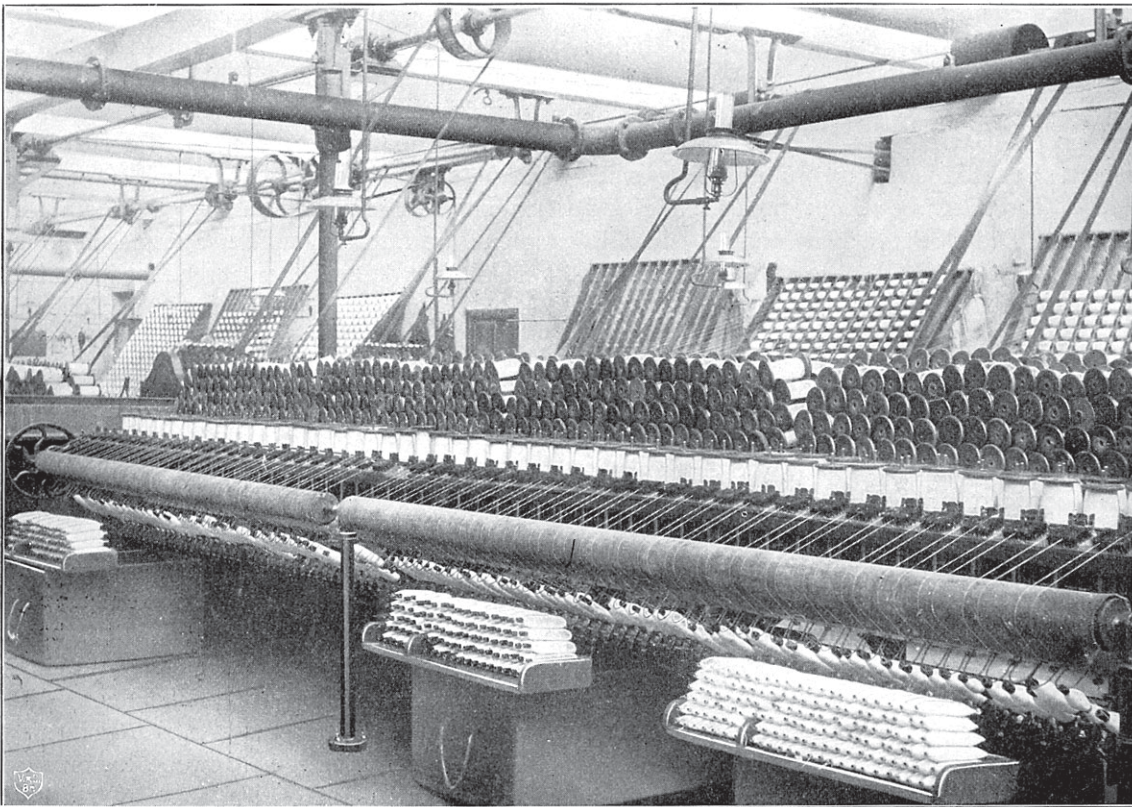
Spulmaschine mit Schermaschinen im Hintergrunde.
